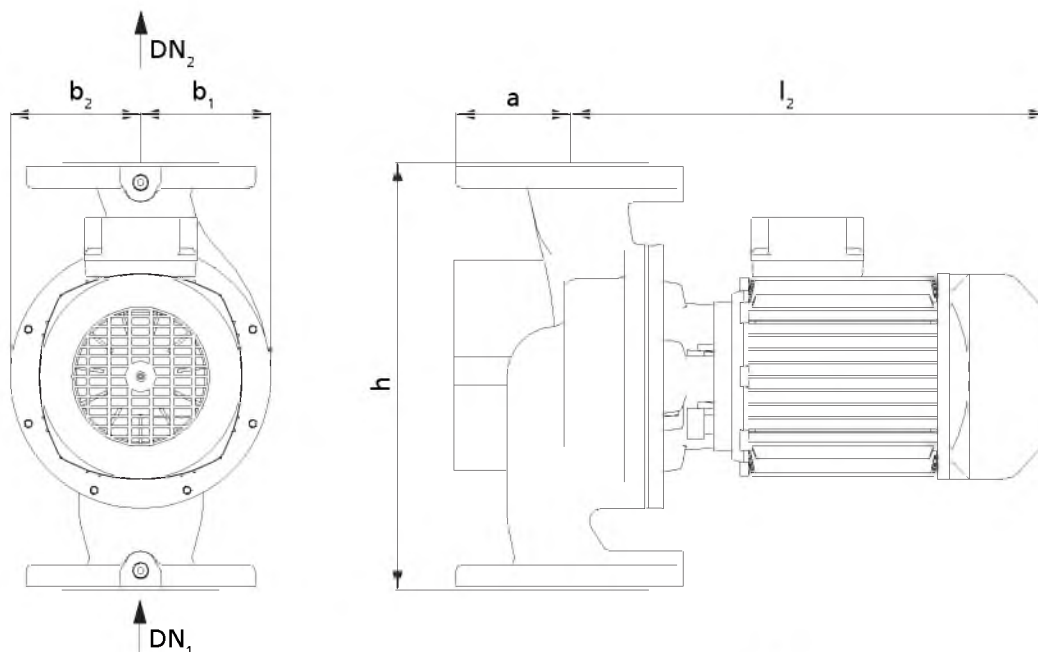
Размеры насосного агрегата с фланцевым соединением, типоразмер ≥ 032-032-100
